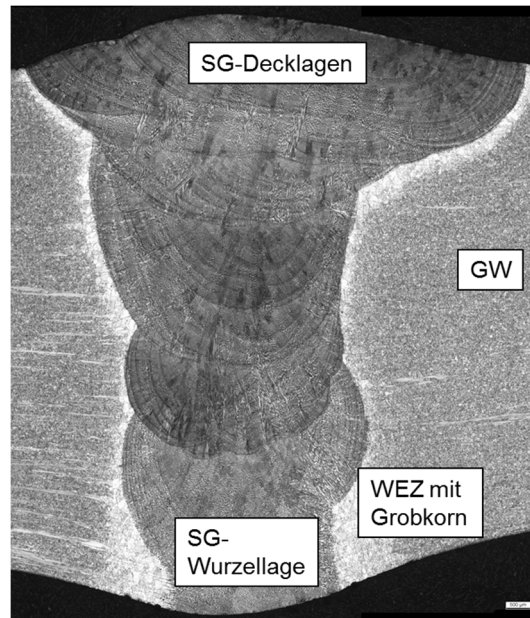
Schliffbild der untersuchten Schweißnaht, Naht wie geschweißt
